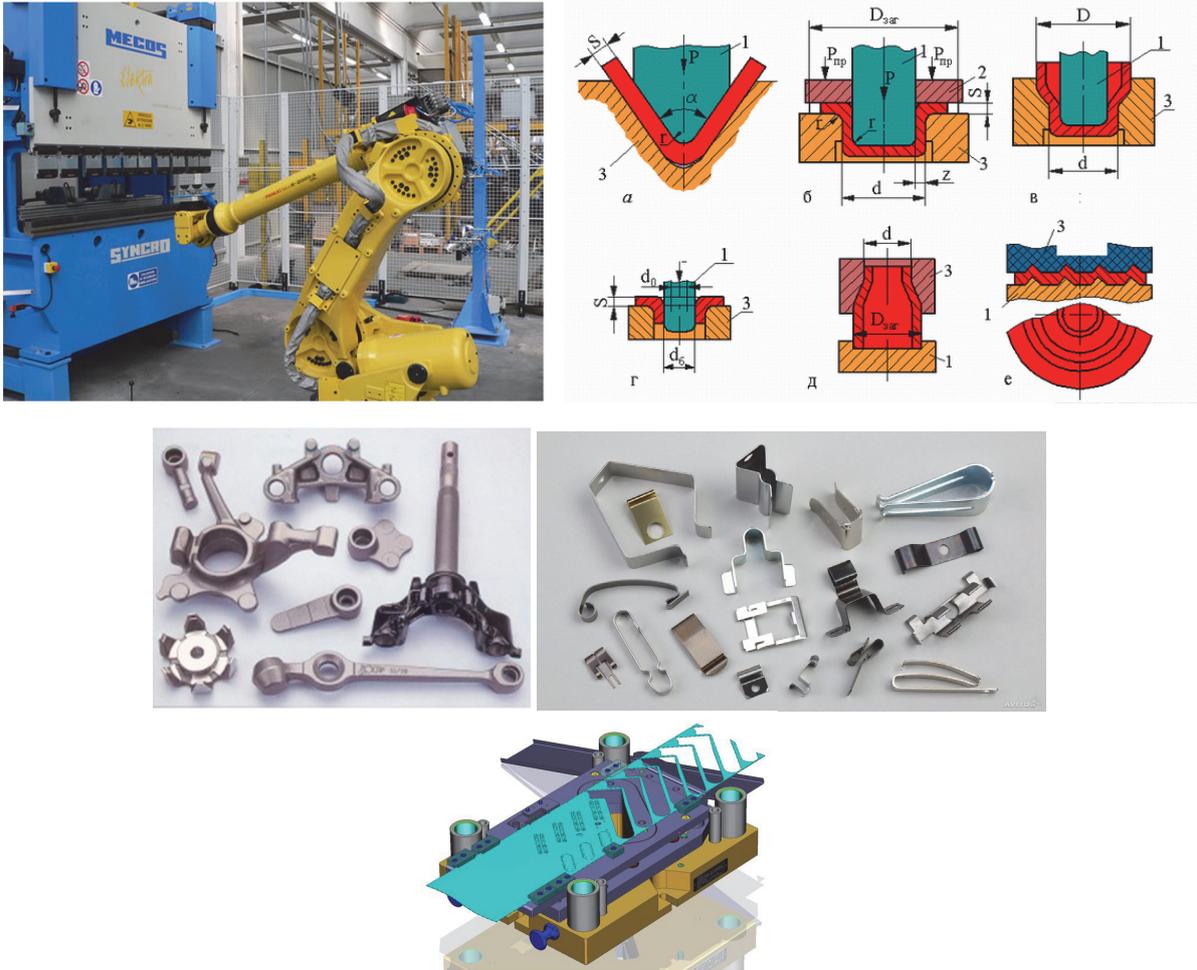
Робот для установки заготовок в компьютеризированный листогибочный пресс, эскизы формообразующих операций, полученные заготовки объемной и листовой штамповки и модель оснастки
